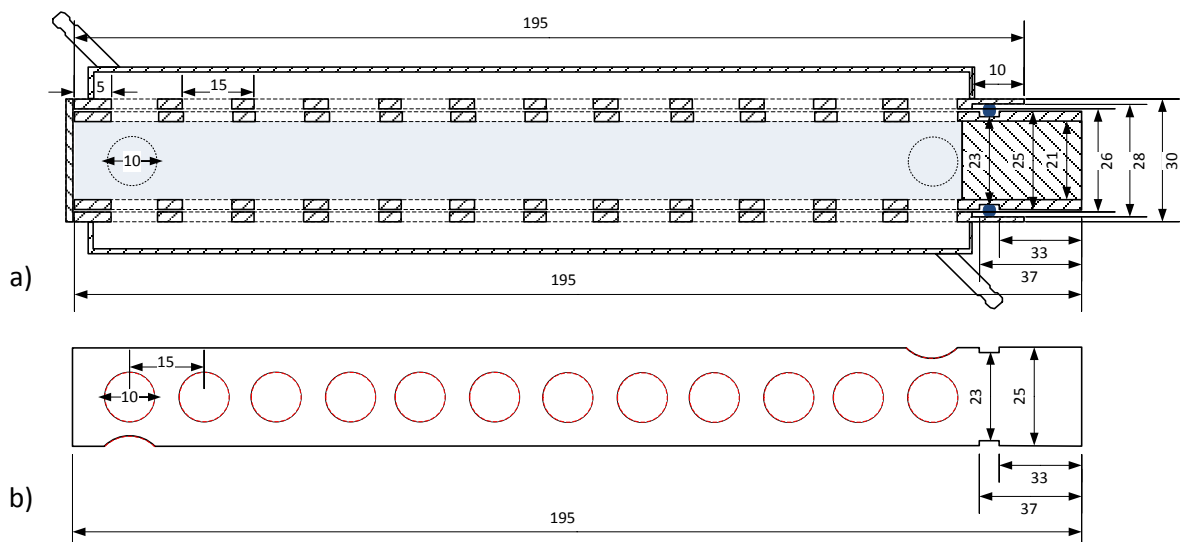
a) Plan der Filtervorrichtung mit allen Massen. b) Skizze des Innenrohrs. Zu beachten sind die beiden um 90° verstellten Löcher.
